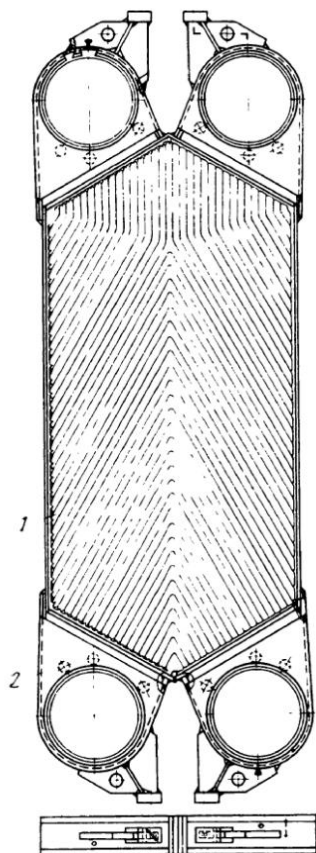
Сварной блок из гофрированных пластин:
